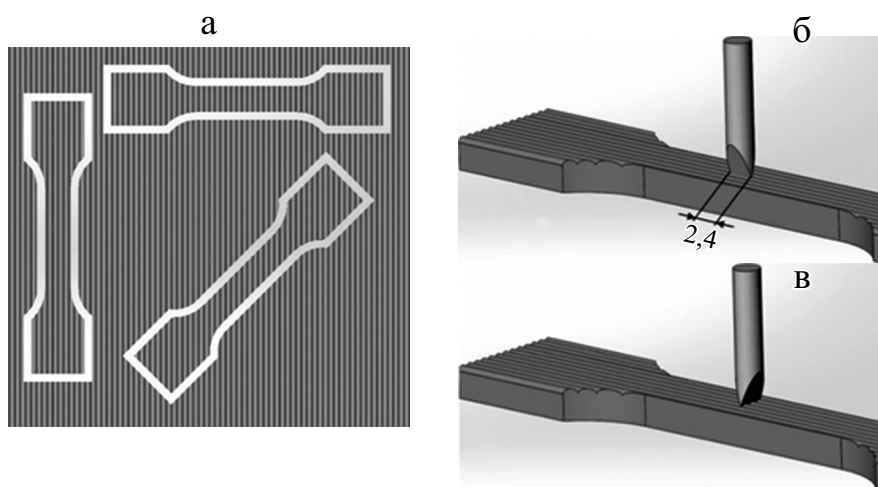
Схематическое представление заготовки для изготовления стандартных образцов на растяжение (а) и схема нагружения образца клиновидным индентором вдоль (б) и поперек плоскости образца (е).
